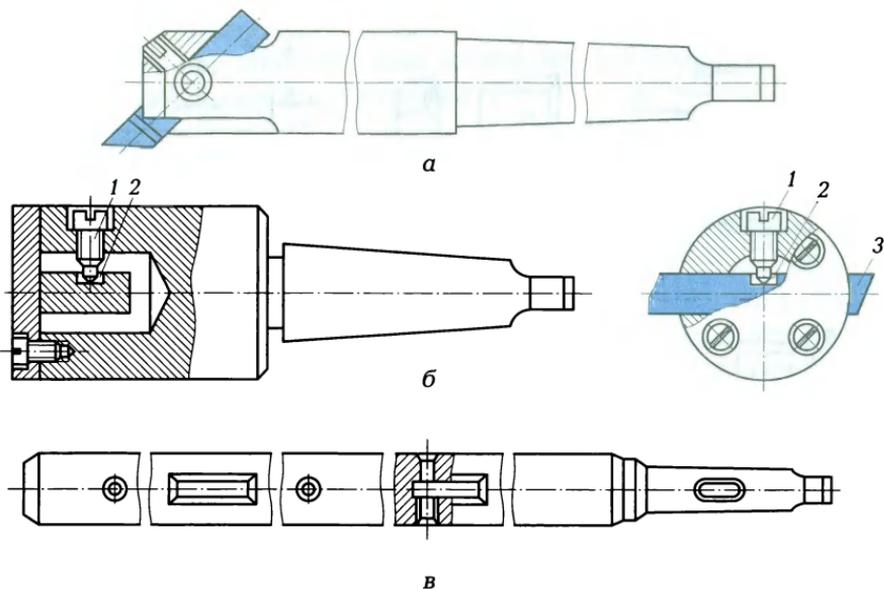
Оправки для закрепления режущего инструмента на расточных станках:
